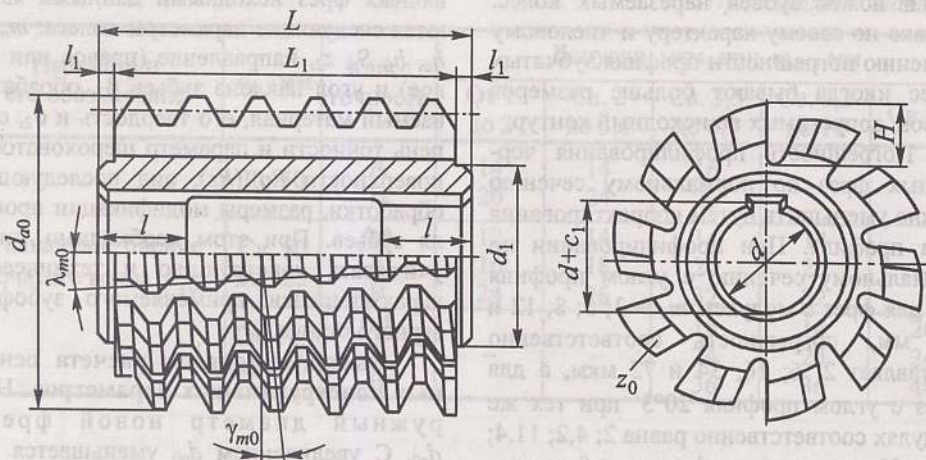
Основные конструктивные размеры цельной червячной фрезы
